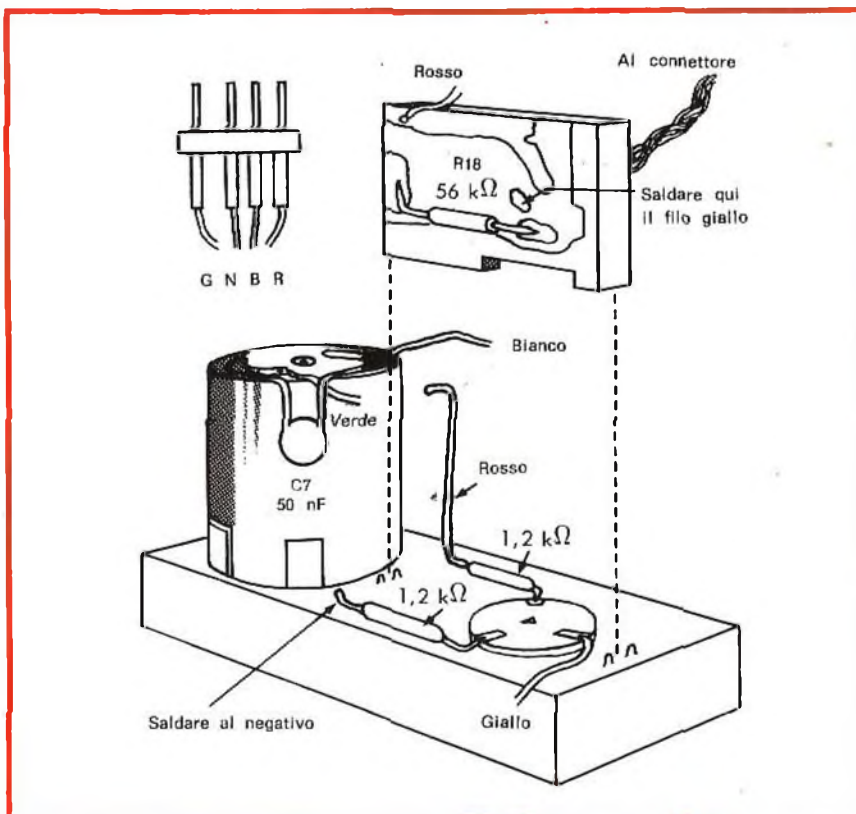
Cablaggio fra il circuito stampato di figura 4 e la parte meccanica del servocomando.
